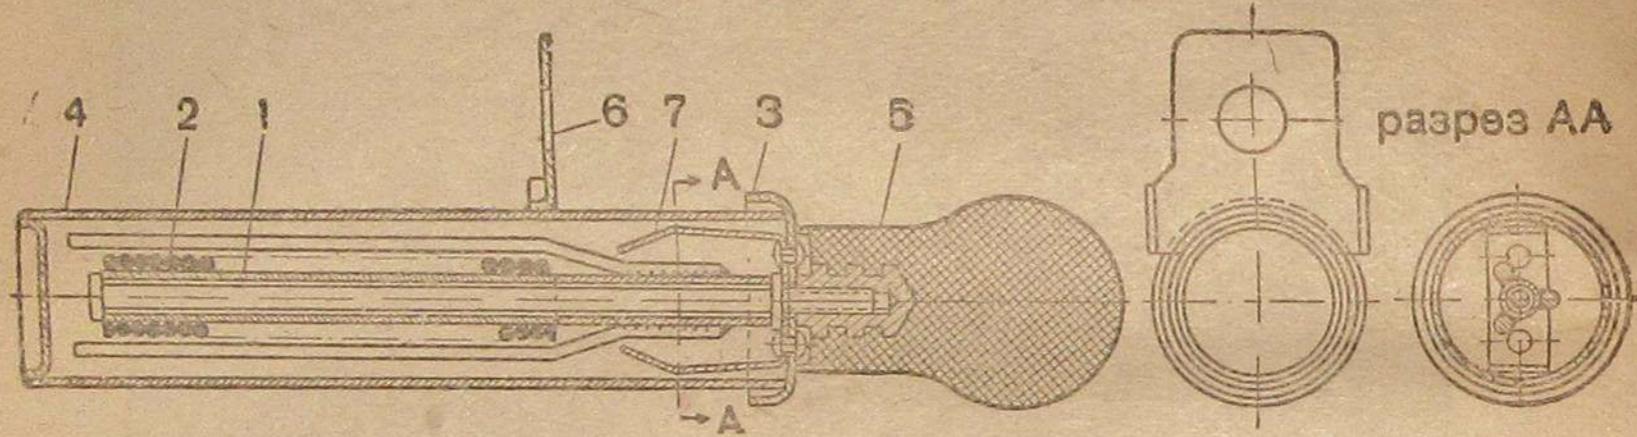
Смеситель для газогенератора НАТИ Г-14
